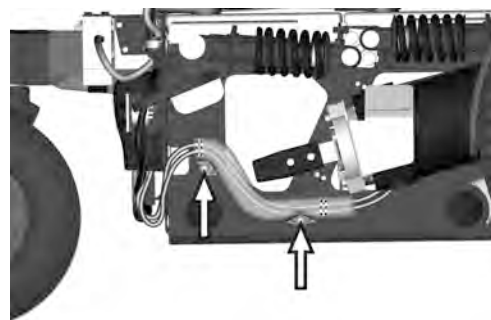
Entfernen Sie die Kabelabdeckung.
